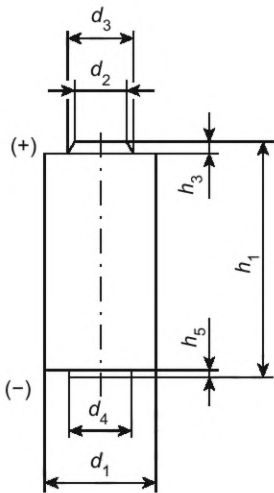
Габаритный чертеж 4LR44, 2CR13252, 4SR44
